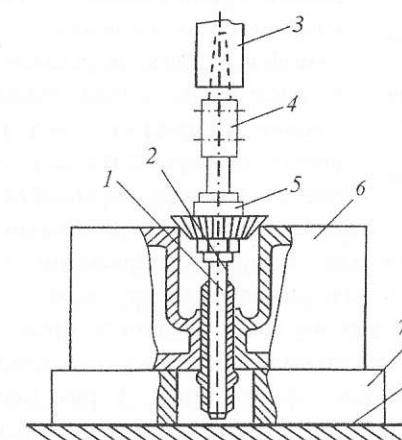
Схема фрезерування ущільнювальної фаски клапанного сідла у кришці циліндра:
